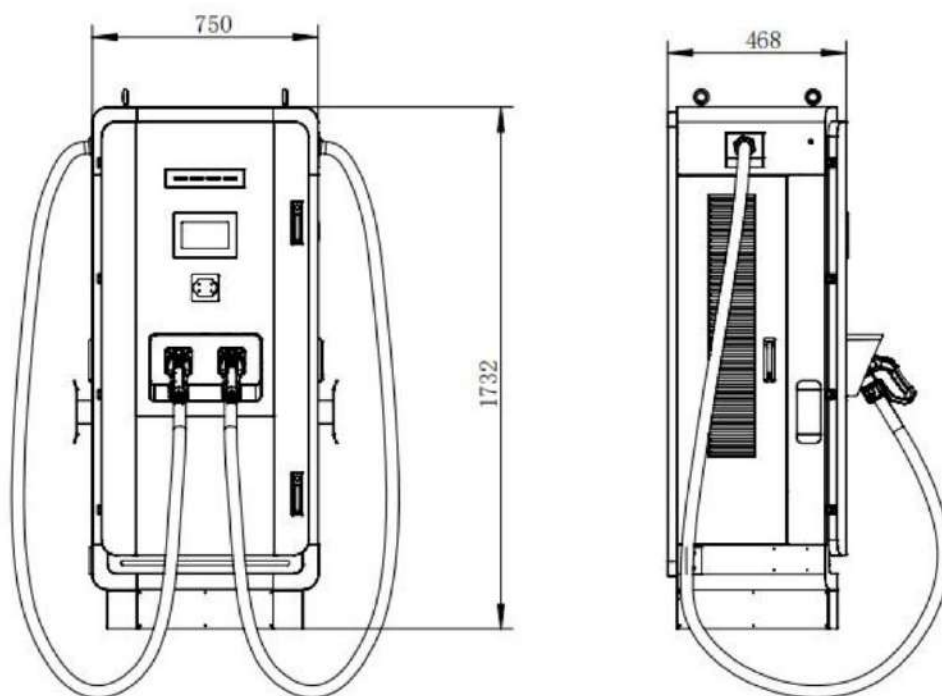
Dimensiones del equipo (MDDC-60kW/80kW)
